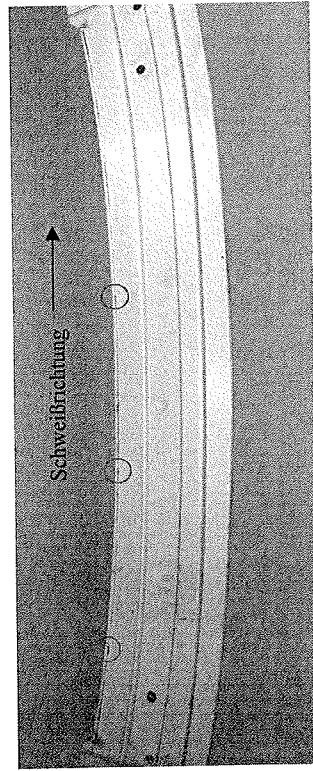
Foto des geschweißten Bauteils mit Markierungen.
